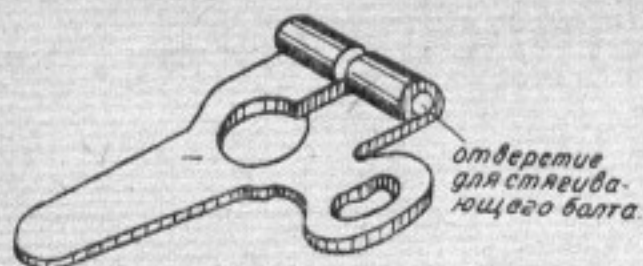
Установочный рычаг прерывателя-распределителя типа ИГЦ автомобиля ЗИС-5
